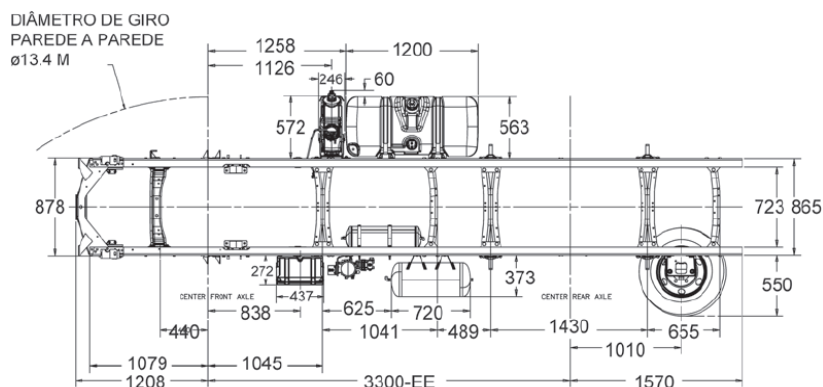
Desenho técnico linha Cargo C-816, Implementador (2013)
